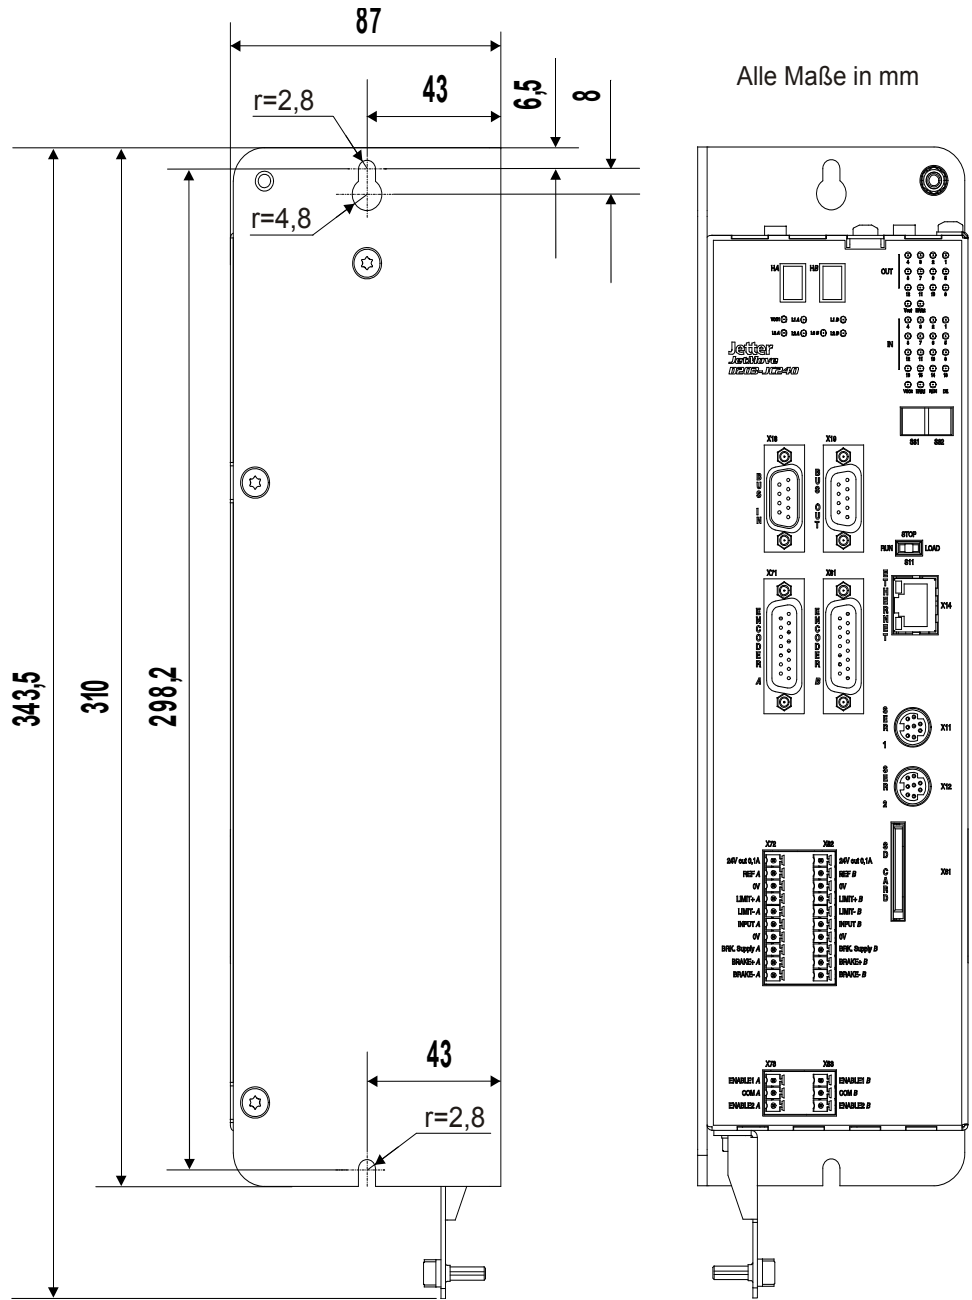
Rück- und Frontansicht des Gehäuses mit Bohrungen
